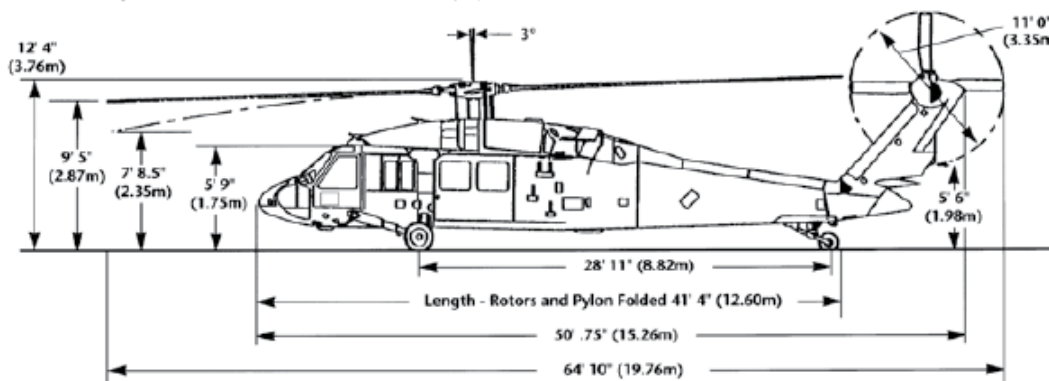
Dimensões do UH 60 – Black Hawk (B ≤ 20m)
